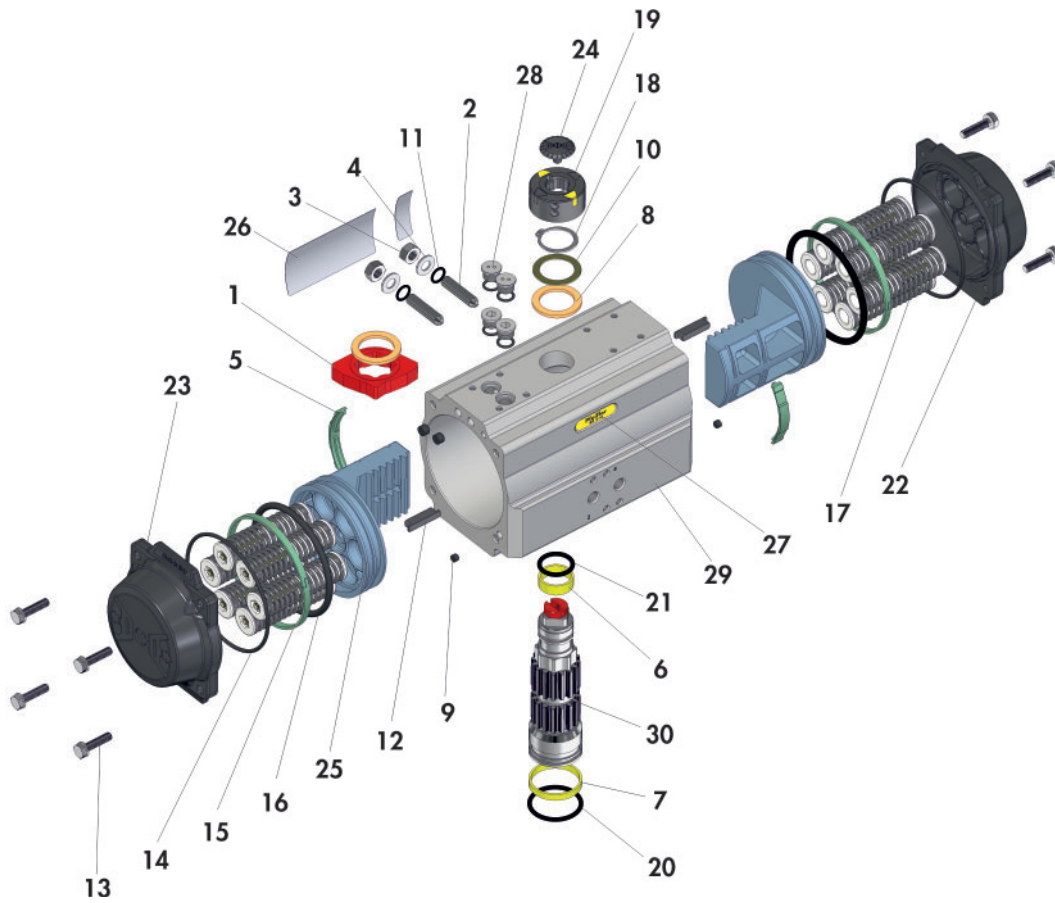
Explosionszeichnung des Schwenkantriebs BR 31a
